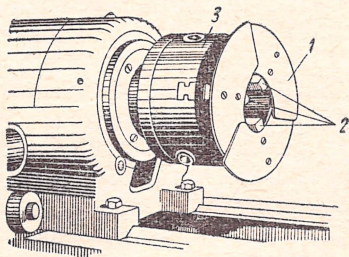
Защитное приспособление к патрону для безопасного полирования деталей
